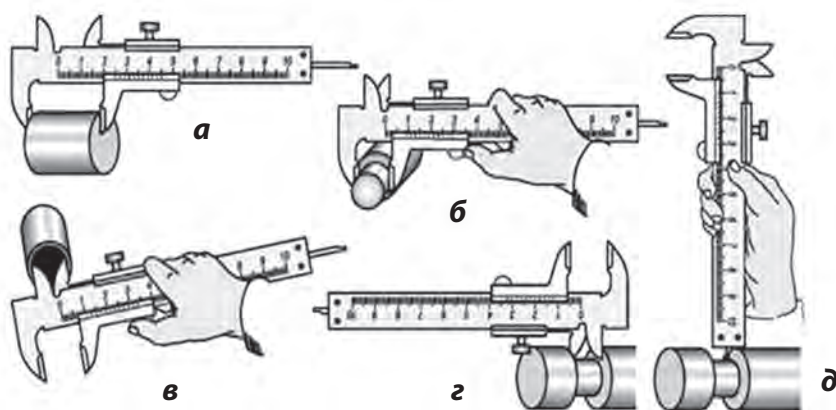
Штангенциркуль ШЦ-I двосторонній з глибиноміром:
